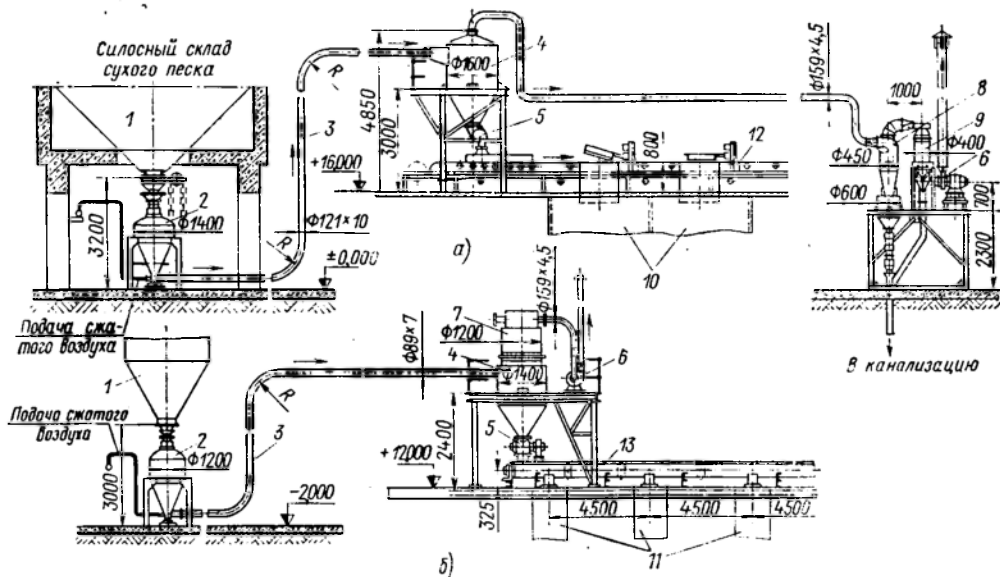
Нагнетательные пневмотранспортные установки с камерными питателями:
